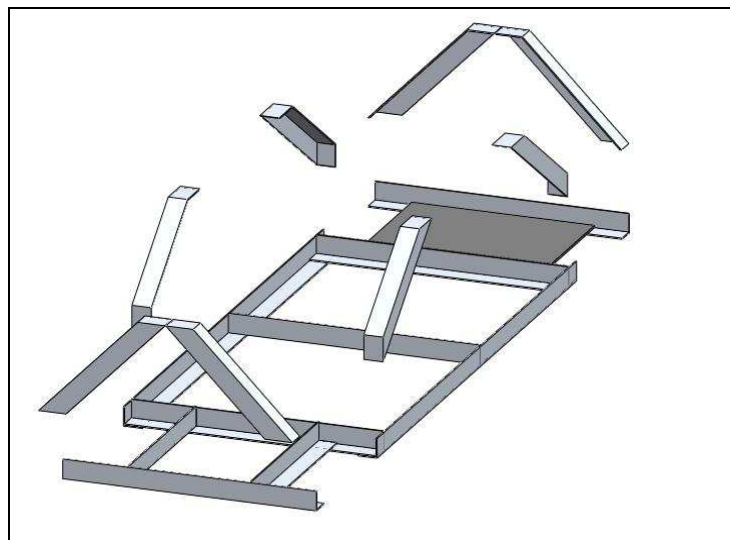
a) Vista explosionada de la sección de unión del bastidor con la sección.
